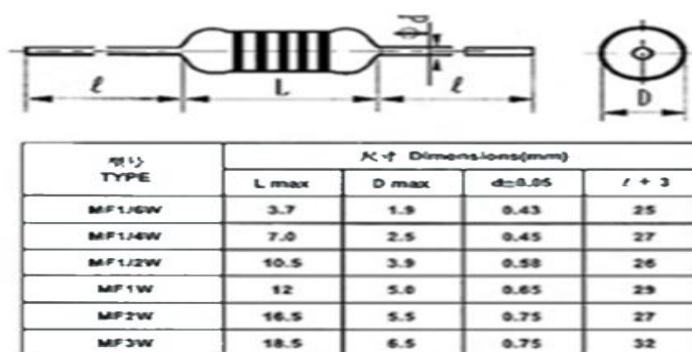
Габаритні розміри резистора MFP-0.5
